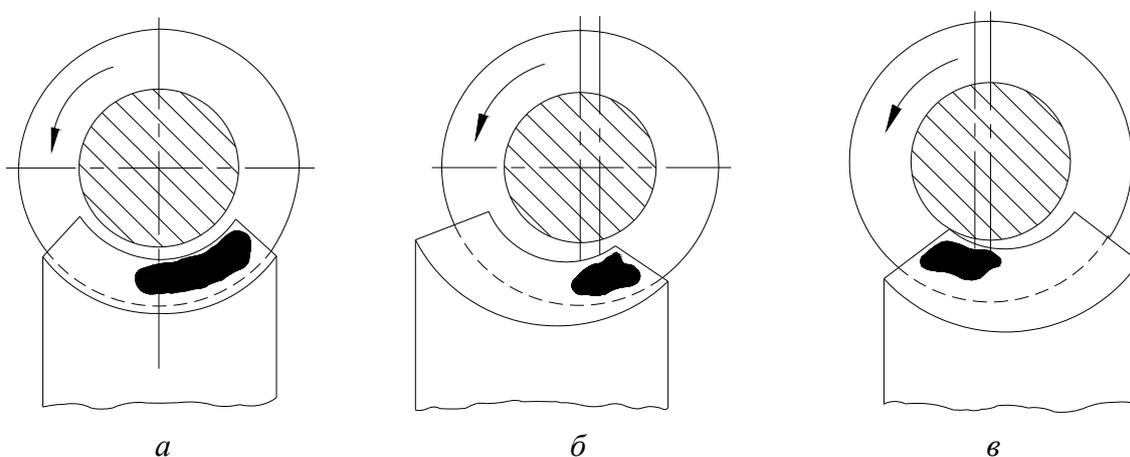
Формы контакта зацепления на зубьях червячного колеса:
